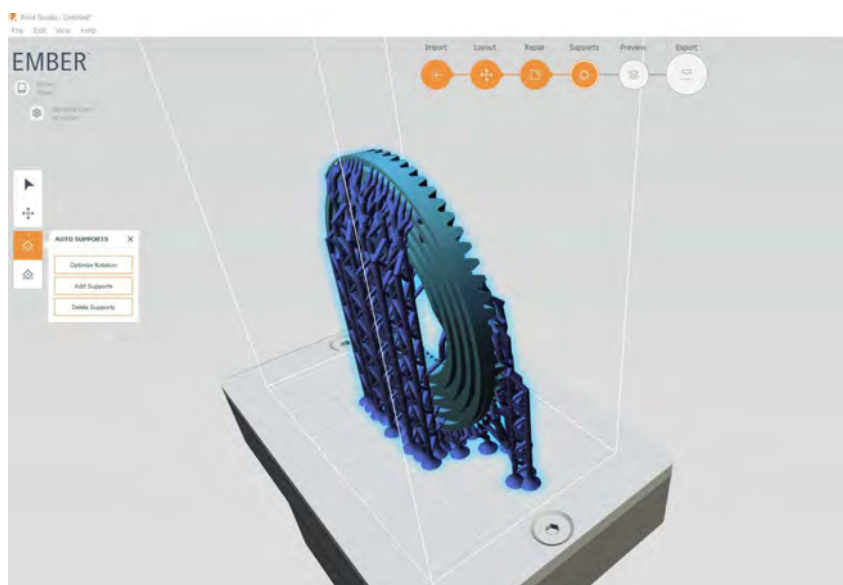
Elementul spiral plan orientat pentru imprimare
